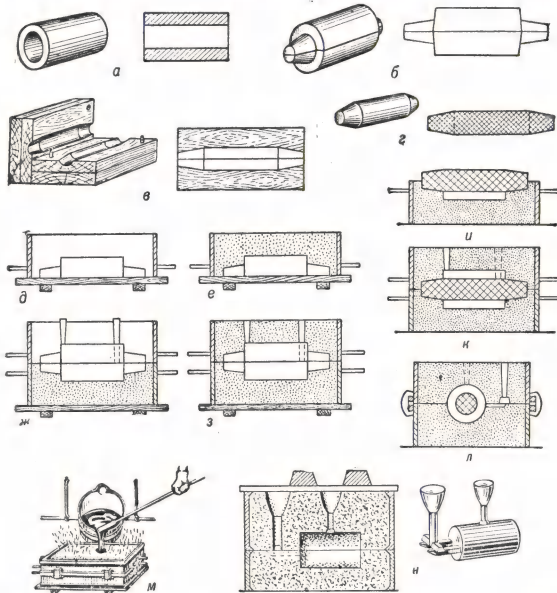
Схема процесса формовки: а — чугунная отливка (втулка); б — деревянная модель втулки; в — стержневой ящик; г — песчаный стержень; д, е — формовка нижней опоки; ж, з — формовка верхней опоки; и — установка стержня в нижнюю полуформу; к — сборка формы; л — сборка под заливку; м — заливка в форму металла; н — литник и выпор в литейной форме и в готовой отливке.
